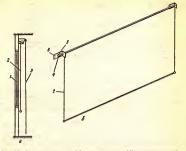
Схема крепления (а) и конструкция (б) солнцезащитной шторы:
